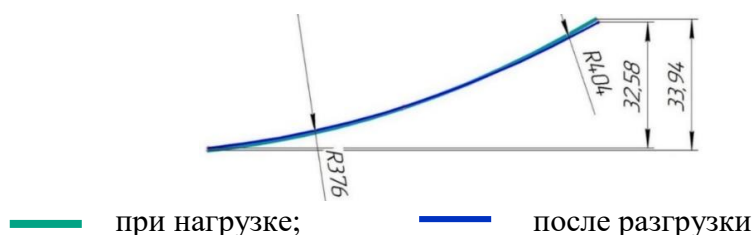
Высота и средний радиус кромки трубной заготовки.
